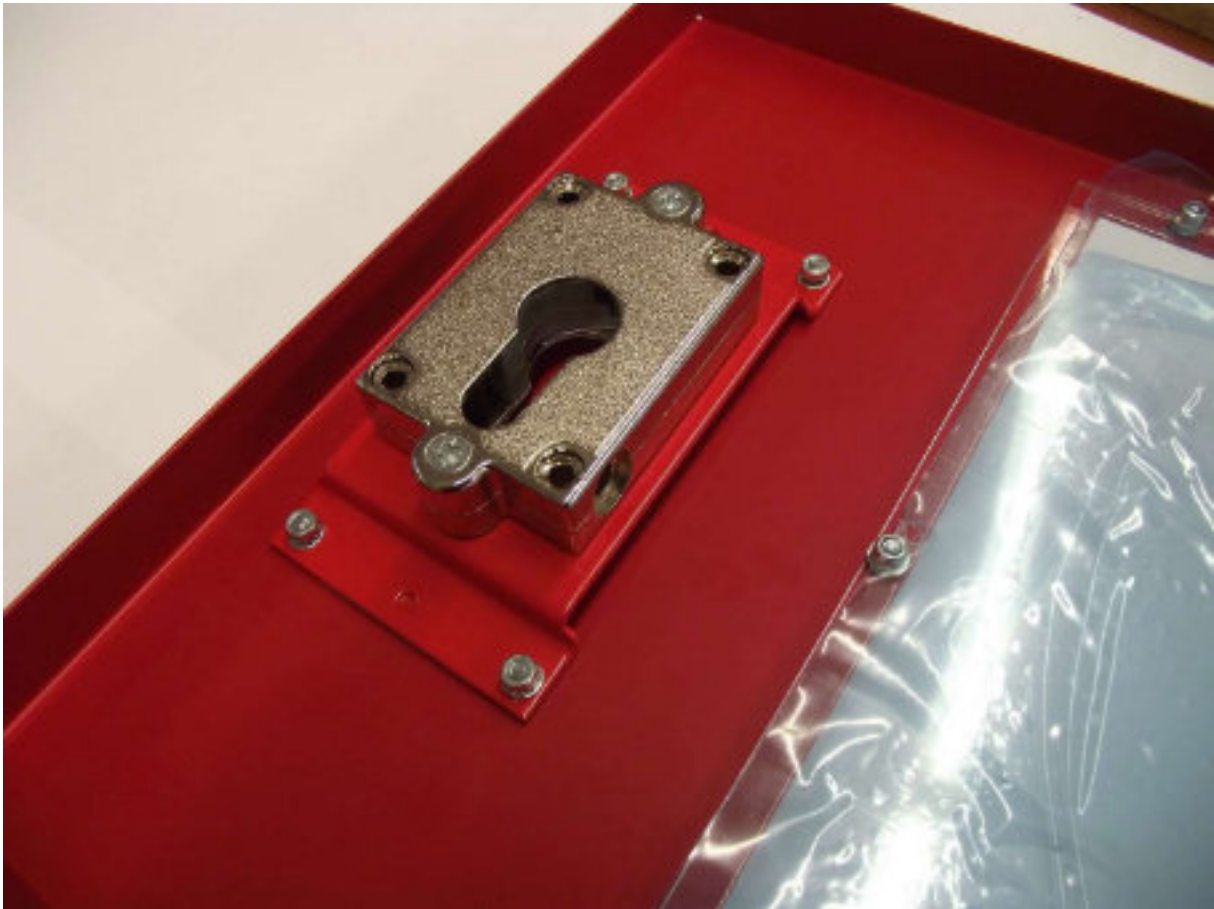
Montiertes Aufnahmeblech für Schließzylinder
